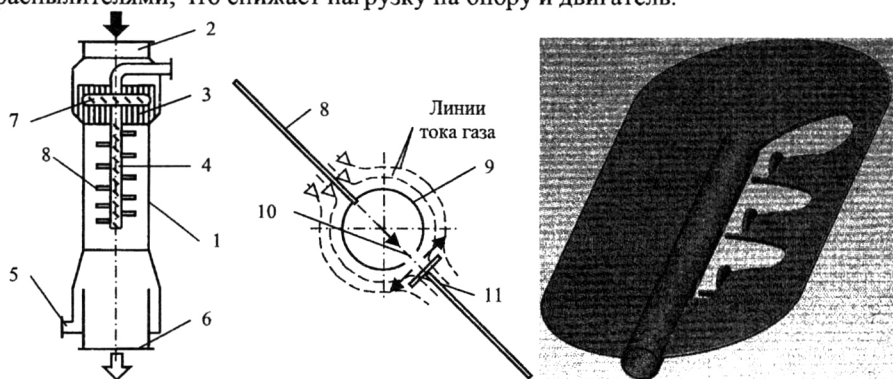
Конструкция вихревого аппарата с ударными пневмогидравлическими распылителями [патент РФ № 102309]: 1 – корпус; 2 – штуцер для входа газа; 3 – завихритель; 4 – центральная труба; 5 – штуцер для выхода жидкости; 6 – штуцер для выхода газа; 7 – ороситель завихрителя; 8 – лопасти; 9 – патрубки; 10 – отверстия; 11 – диски
